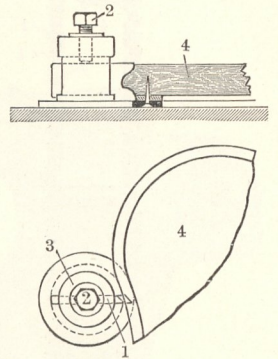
Fräser einer Holzfräsmaschine (Fräsen eines Profils nach Schablone).
